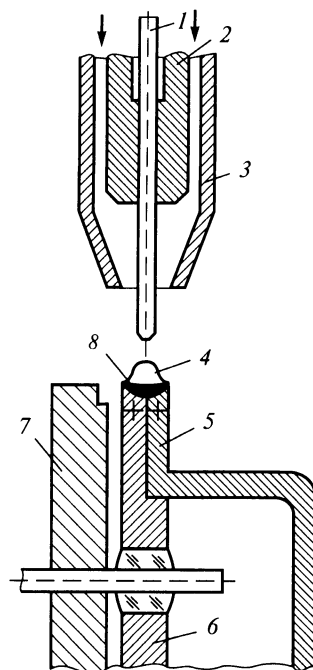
Схема образования сварного соединения при герметизации корпусов аргонно-дуговой сваркой:
